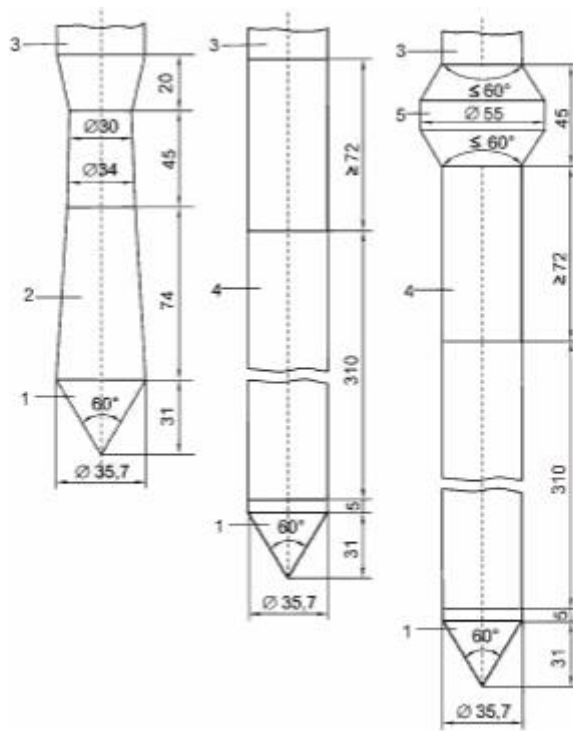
Зонды для статического зондирования I , II и III типа: 1 – конус; 2 – кожух; 3 – штанга; 4 – муфта; 5 – уширитель (Мариупольский Л.Г., 1989) [11].
